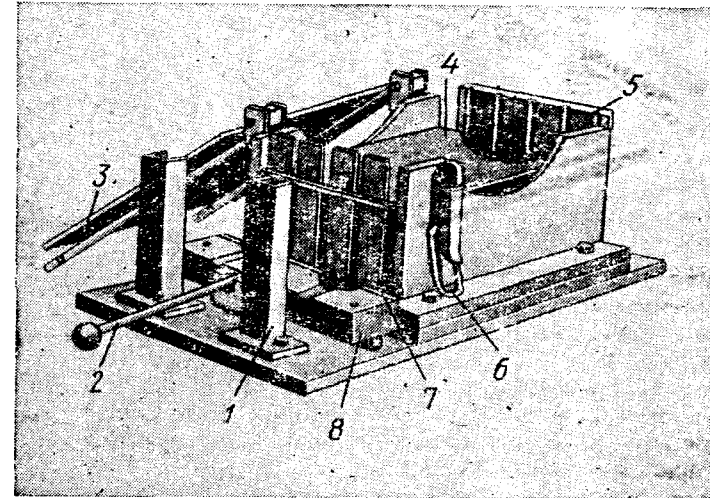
Приспособление для сборки блока ламельных пластин: 1 — стойка, 2 — рукоятка, 3 — крышка на шарнирах, 4 — подвижное дно на пружинах, 5 — задняя стенка, 6 — защелка с серьгой, 7 — передняя стенка, 8 — колодка
